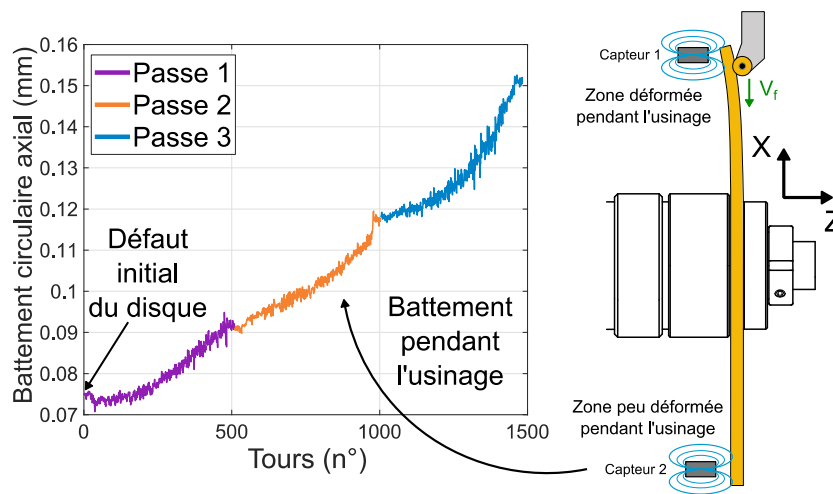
Evolution in-process du battement circulaire axial proche du diamètre extérieur du disque causé par l'introduction de CR d'usinage dans la ZAPU et le rééquilibrage des CR pré-usinage -  $V_c = 35$  m/min,  $f = 0.1$  mm/tr,  $a_p = 0.5$  mm.
